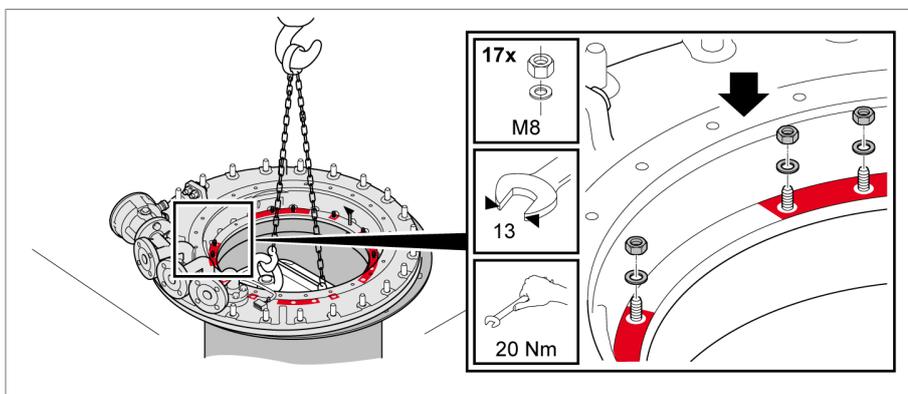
Крепление головки устройства РПН к опорному фланцу
